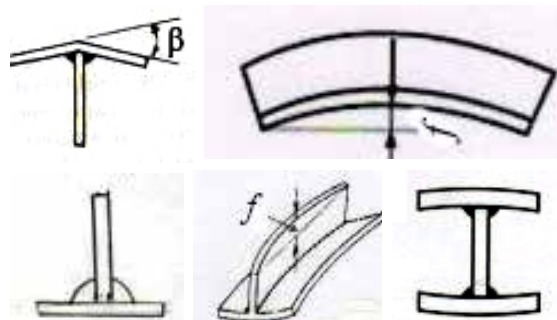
Некоторые виды деформации изгиба при сварке длинных изделий; f – стрелка прогиба
